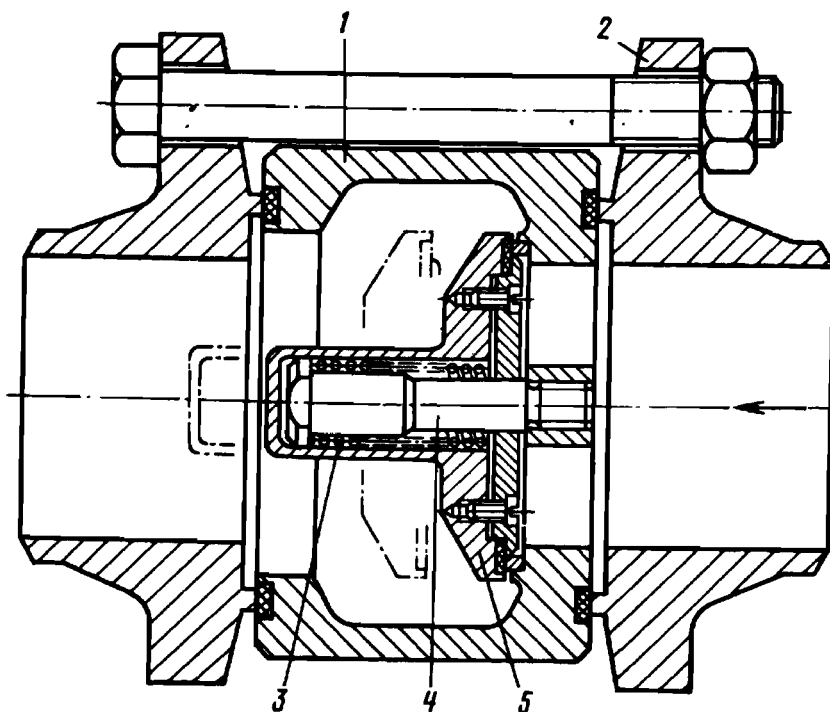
Прямоточный обратный клапан зажимной конструкции:
